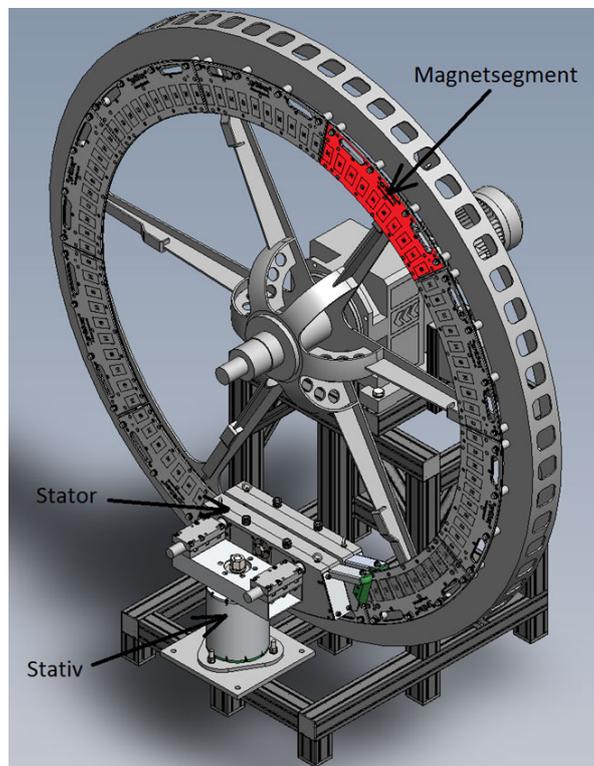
Versuchsstand mit Ringsegmentgenerator
